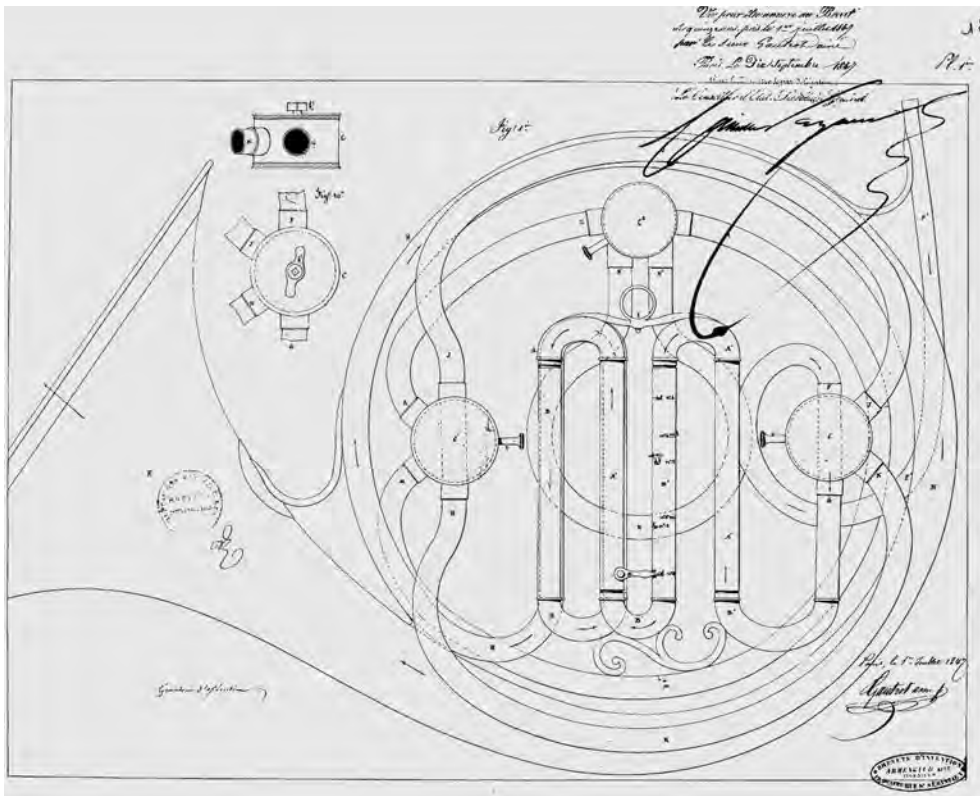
Dessin du brevet 5874 du 1^{er} juillet 1847, planche 1
